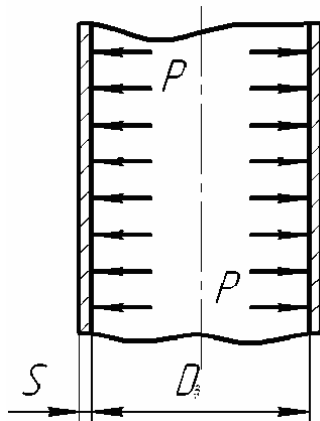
Розрахункова схема циліндричної обичайки
